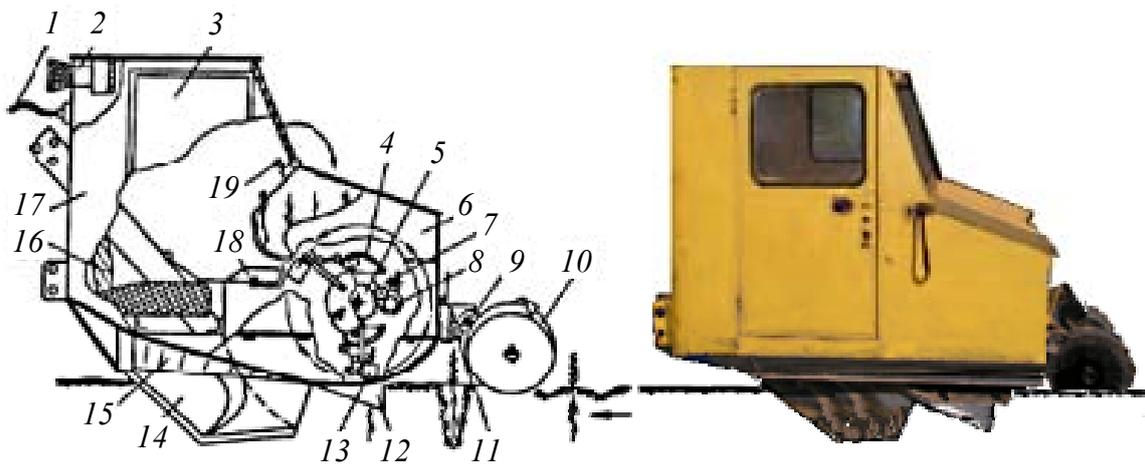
Схема лесопосадочной машины ЛМД-21: 1 – электропривод; 2 – вентилятор с фильтром; 3 – дверь; 4 – лекало раскрывателя захватов; 5 – зубчатое колесо вала посадочного аппарата; 6 – бункер для посадочного материала; 7 – бортовая электросеть; 8 – электродвигатель постоянного тока; 9 – крестовина; 10 – прикатывающие катки; 11 – храпово-пружинный механизм регулирования давления катков на почву; 12 – заделывающие клинья; 13 – захват; 14 – сошник; 15 – опорная пластина; 16 – сиденье сажальщика; 17 – кабина; 18 – приемный столик для сеянцев; 19 – панель управления электроприводом
